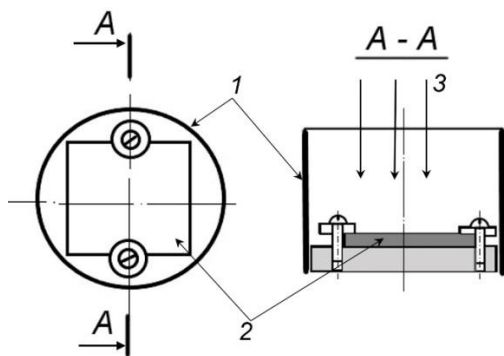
Приспособление для облучения образцов ванадия потоками ионов и плазмы:
